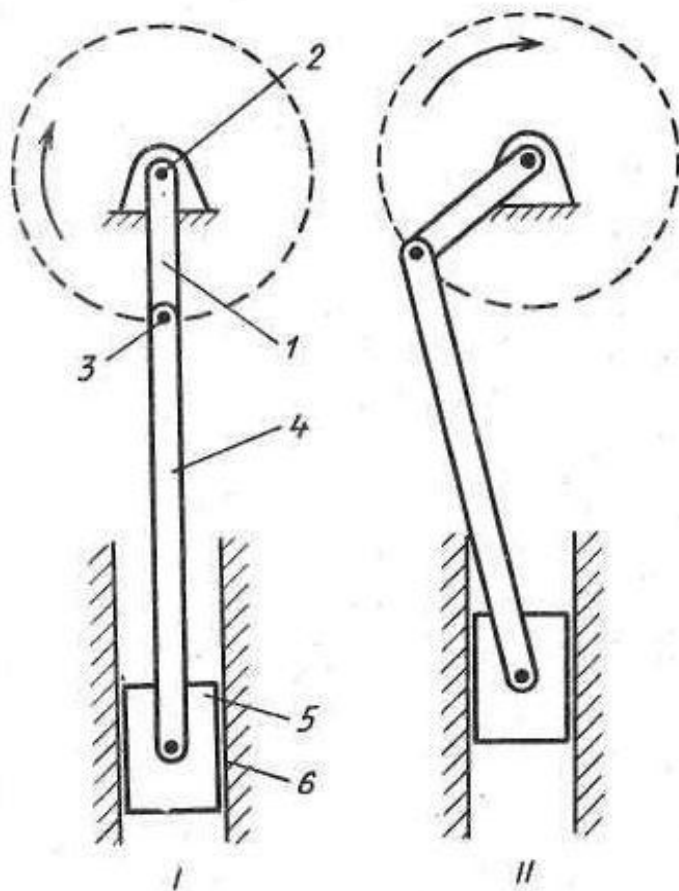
Схема принципу роботи кривошипно-шатунного механізму: 1 — кривошип, 2 — головний вал, 3 — палець кривошипу, 4 — шатун, 5 — повзун, 6 — направляючі [16]
